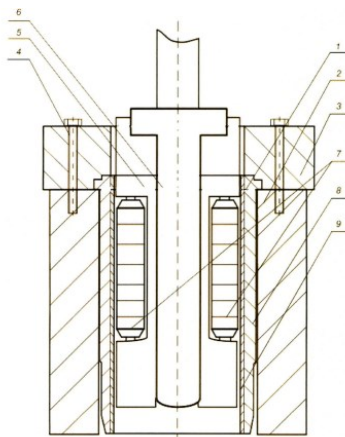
Приспособление для проведения ФАБО гильз цилиндров
